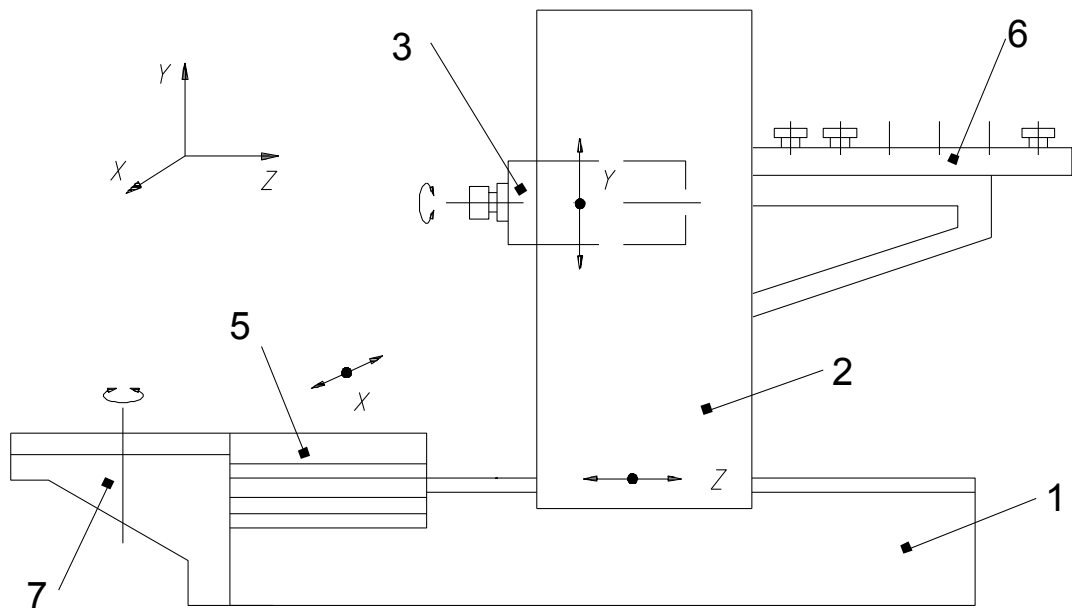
Багатоцільовий верстат з ЧПК моделі BEA2 фірми Heller (Німеччина)
